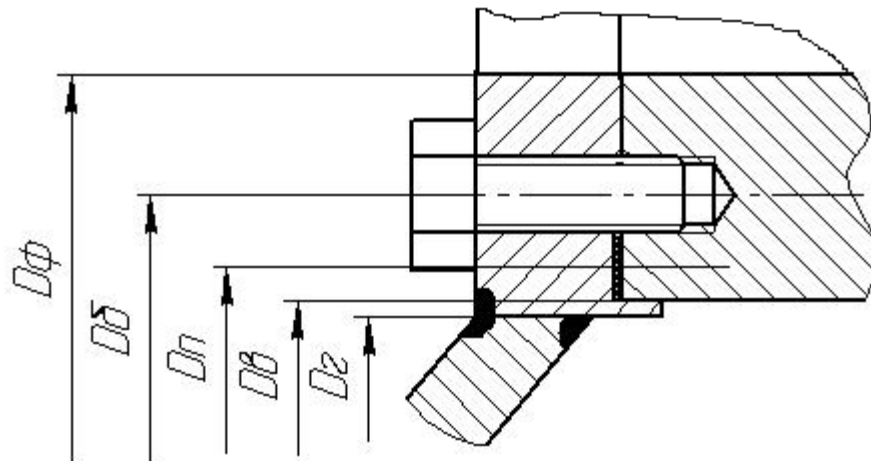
Розрахункова схема фланцевого з'єднання
